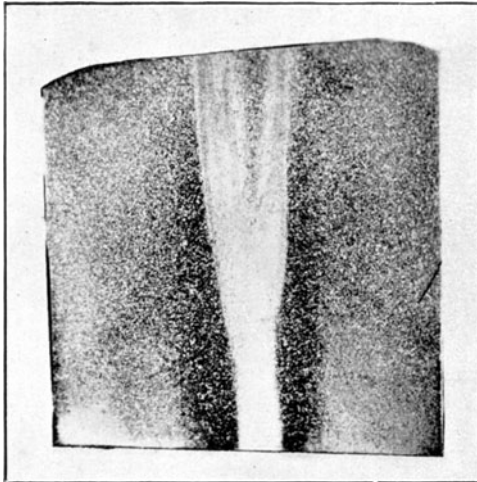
Längsschnitt einer Stahlstange aus einem Gußblock mit hochgekohltem Kern.
